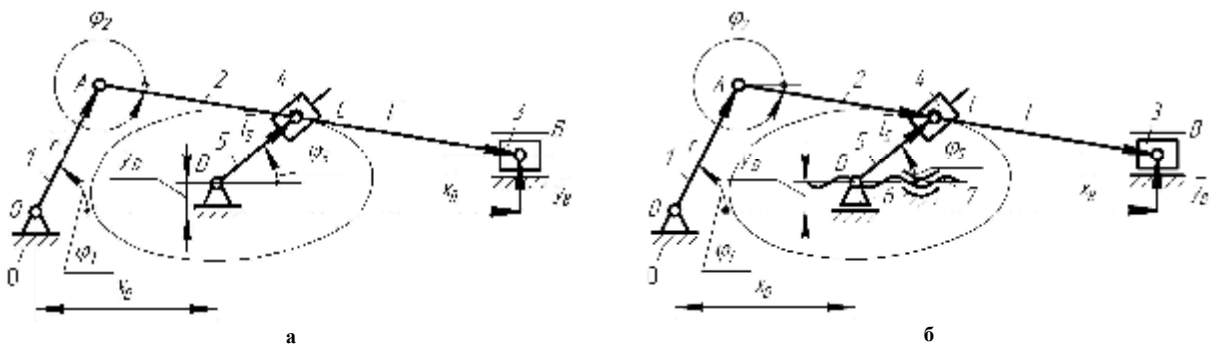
Двокривошипний шарнірний чотириланковий механізм: а)  $a = \text{const}$ ; б)  $a \neq \text{const}$
